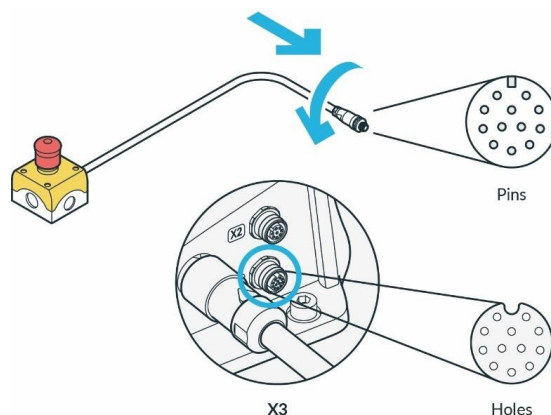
Collegamento del dispositivo di protezione (in questo caso dispositivo di comando di arresto di emergenza
